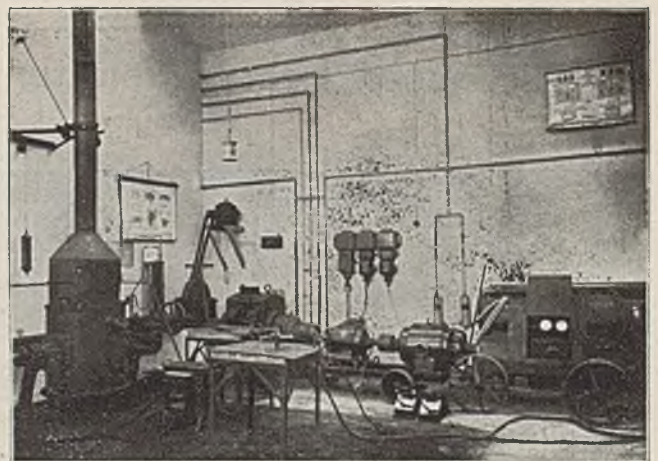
Elektro-Schweißwerkstatt.
